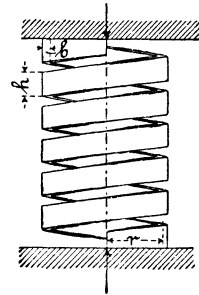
Zylindrische Schraubenfeder mit rechteckigem Querschnitt.
